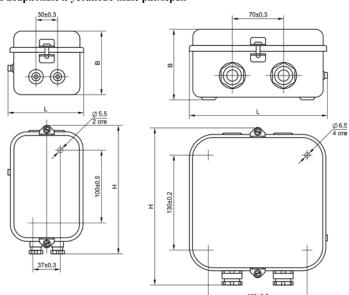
Габаритные размеры	Рисунок 2. Габаритные размеры
